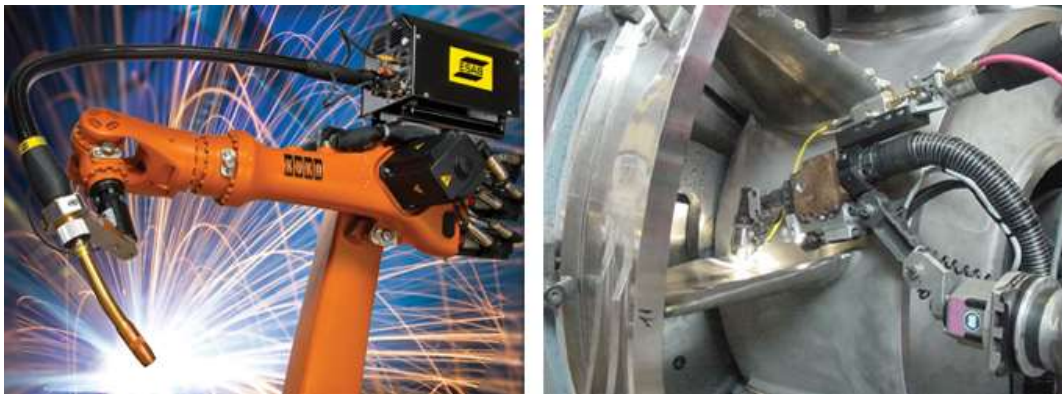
Soldadura robotizada, a la derecha detalle de soldadura en una pieza de una turbina aeronáutica.
